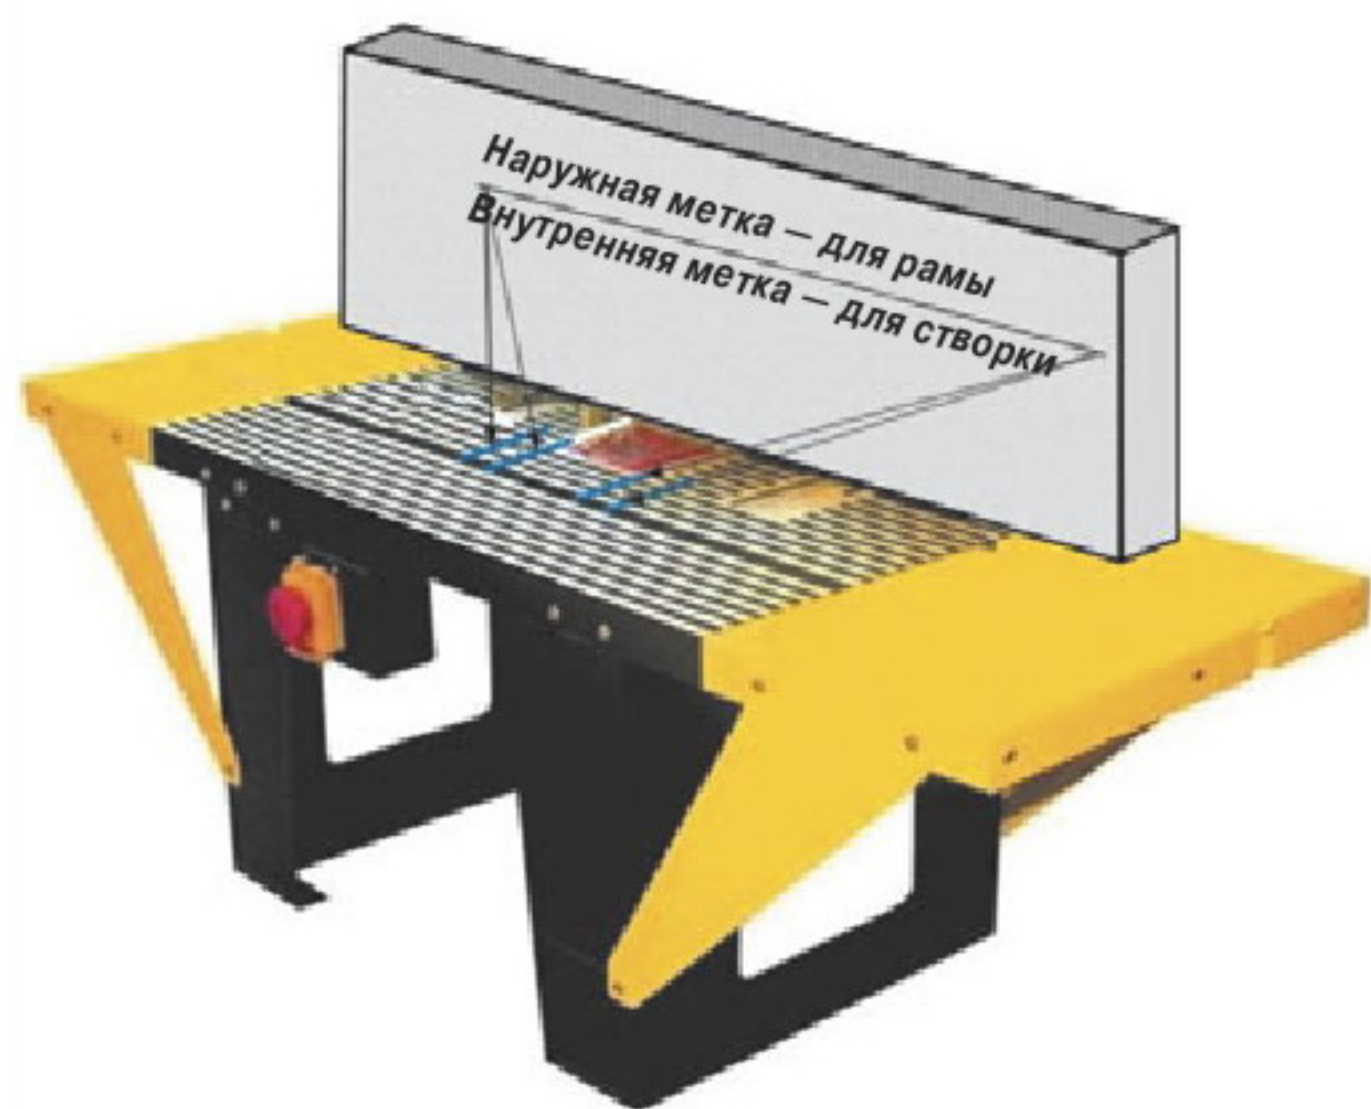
Для выборки пазов использовал фрезерный стол Корвет-80. Для удобства пришлось нарастить боковой упор.
